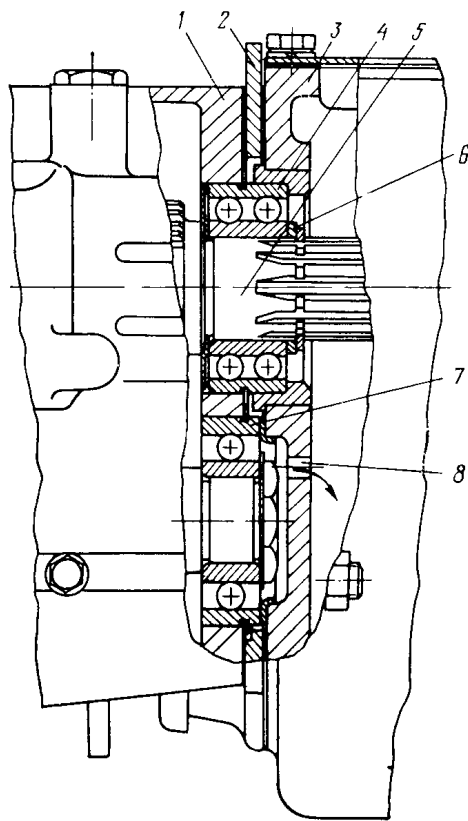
Установка заднего подшипника и ведомого вала в картер коробки передач автомобиля УАЗ-452: 1 — картер коробки передач; 2 — пластина крепления раздаточной коробки и коробки передач; 3 — картер раздаточной коробки; 4 — задний подшипник ведомого вала; 5 — ведомый вал; 6 — упорное кольцо; 7 — задний подшипник промежуточного вала; 8 — отверстие для слива масла
